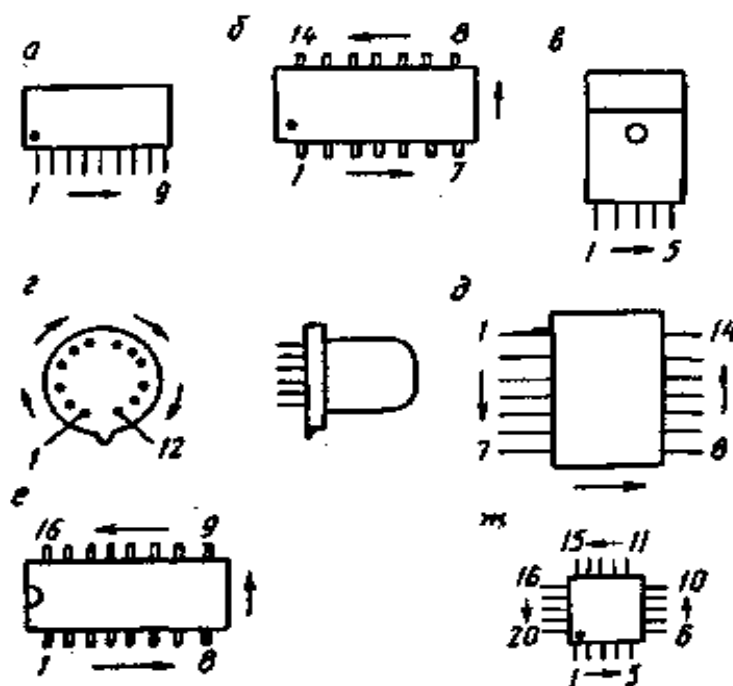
Корпуса микросхем (а-ж) и порядок нумерации выводов
